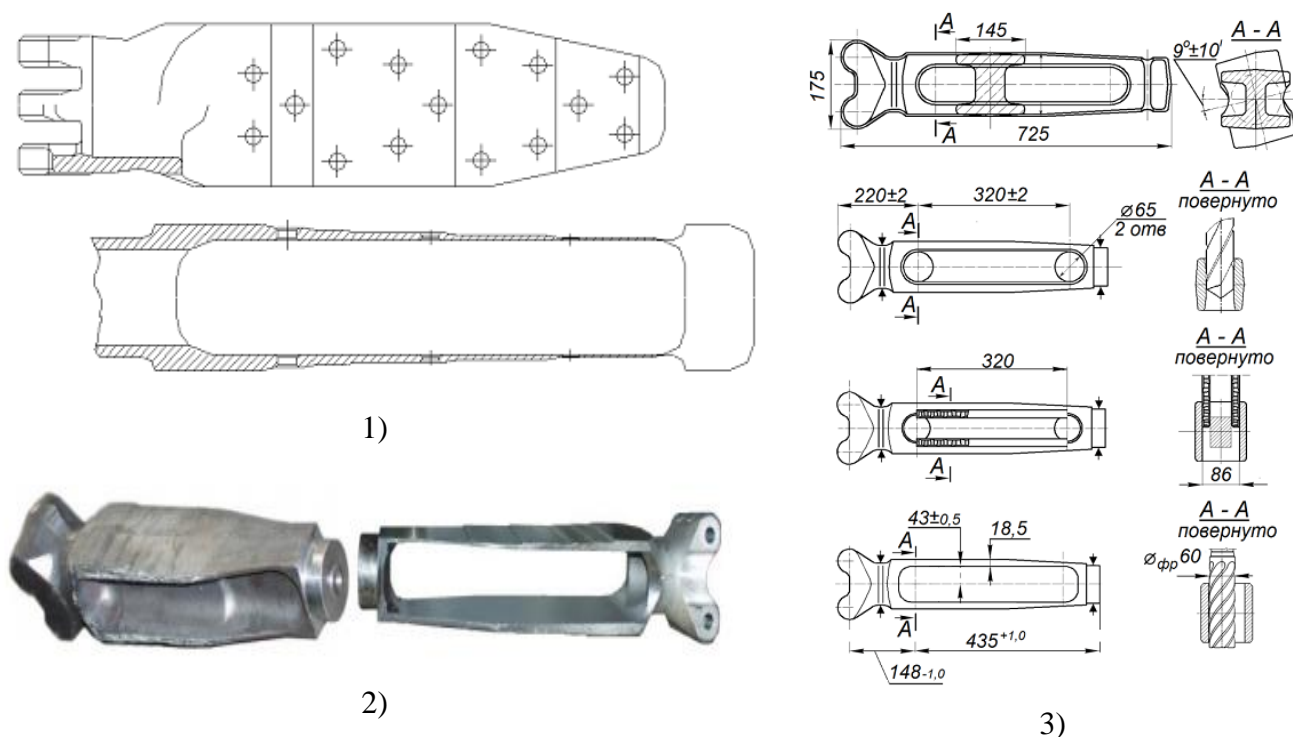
Пример детали: 1 — эскиз; 2 — фото заготовки; 3 — операционные эскизы обработки наконечника лопасти несущего винта
